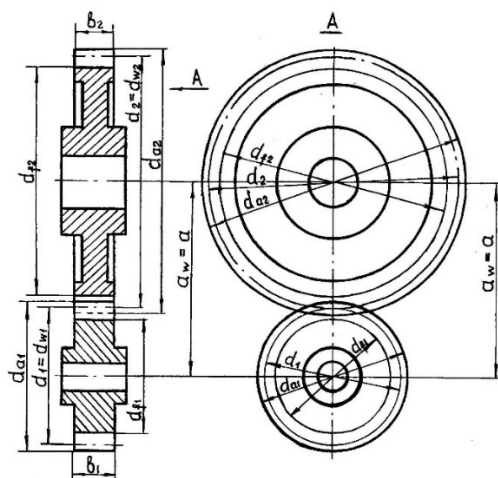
Dessin d'un engrenage droit avec les dimensions principales.
